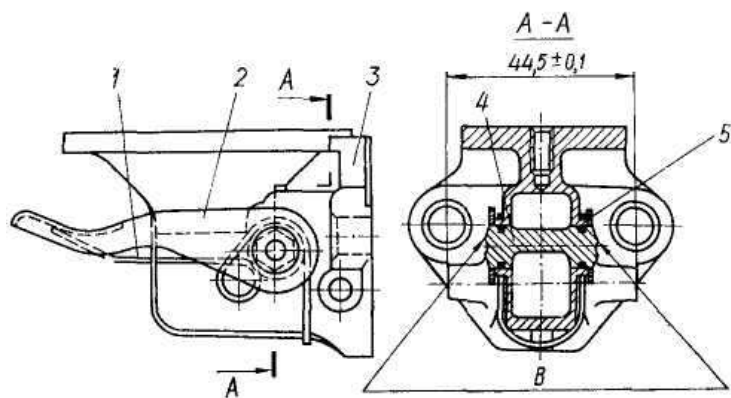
Нижний корпус топливного насоса в сборе: 1 — пружина рычага; 2 — рычаг; 3 — нижний корпус; 4 — эксцентрик; 5 — кольцо уплотнительное; В — указанные места расклепать и загладить
